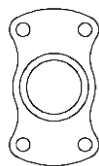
Вид детали «Сверху» без размеров и осевых линий
